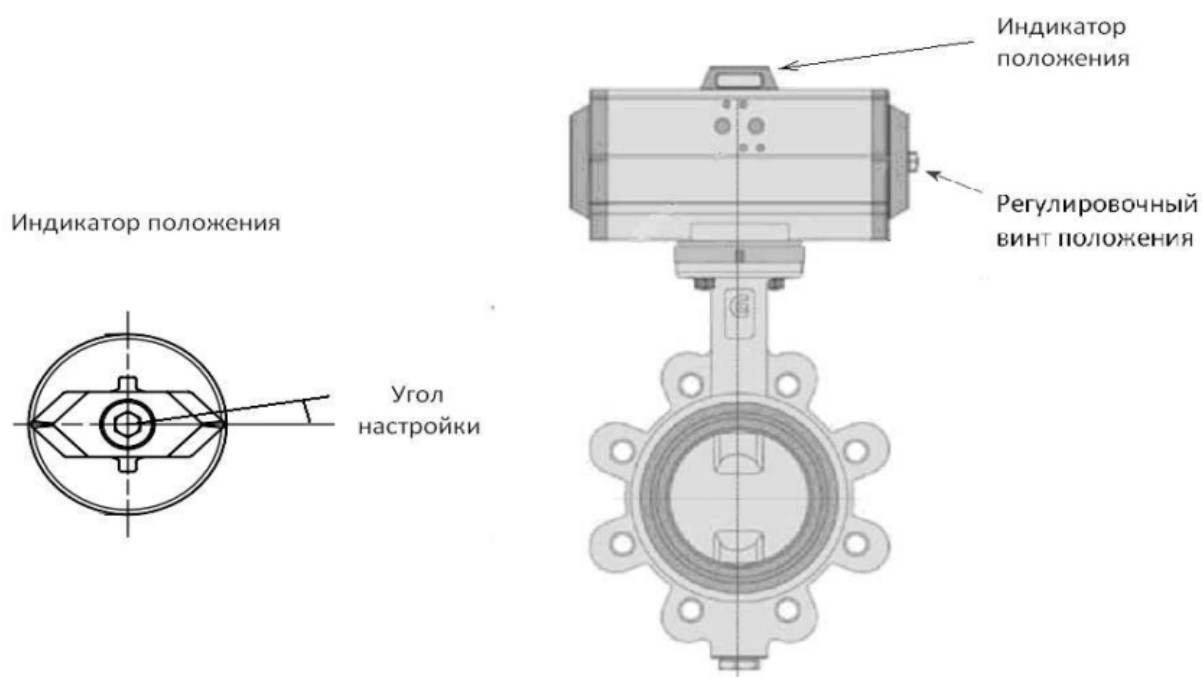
Регулировка положения пневмопривода и дискового затвора.
